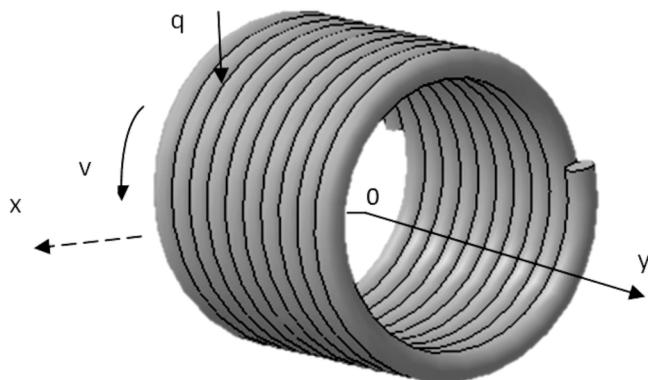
Схема лазерной сварки витков пружинно-витого канала
